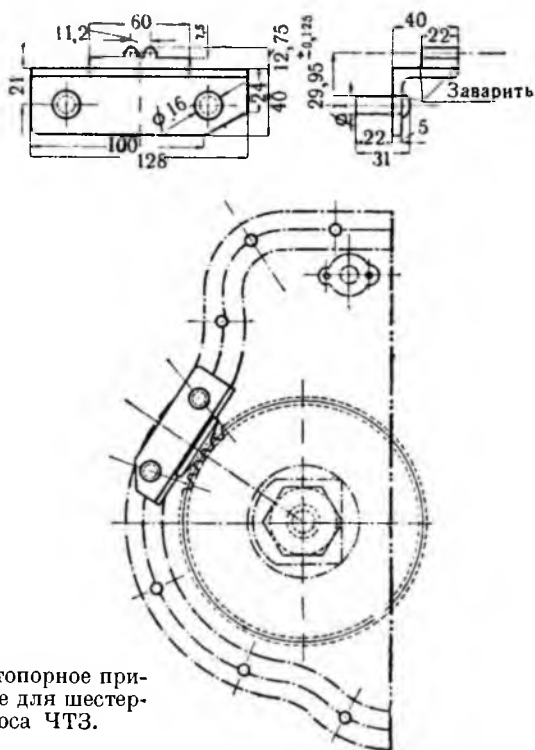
Стопорное приспособление для шестерни насоса ЧТЗ.
